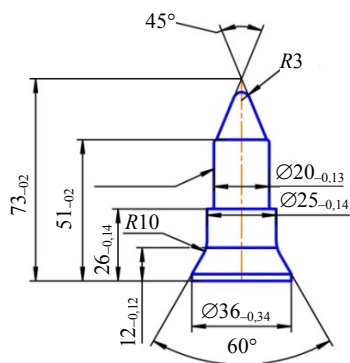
Чертеж детали пуансон № 9783-433.09 из номенклатуры инструментального производства ОАО «МАЗ»
